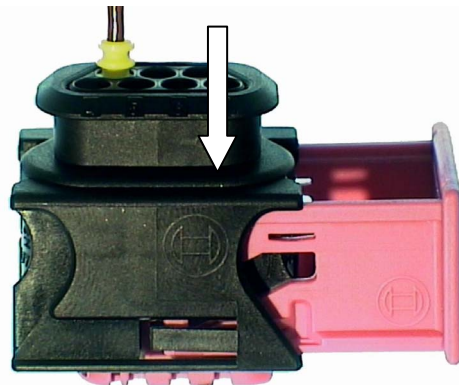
Kontaktmontage (Trapezstecker 7-polig mit Schieber)
